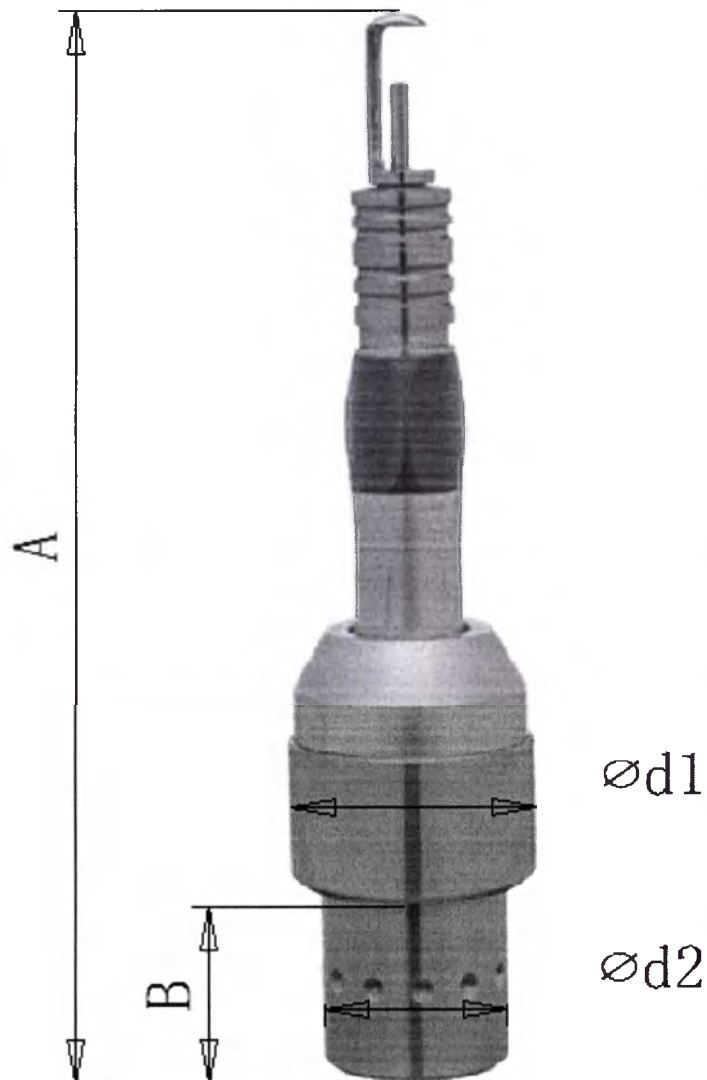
Насадка - бур краниальный АЛЬФА-10.04
